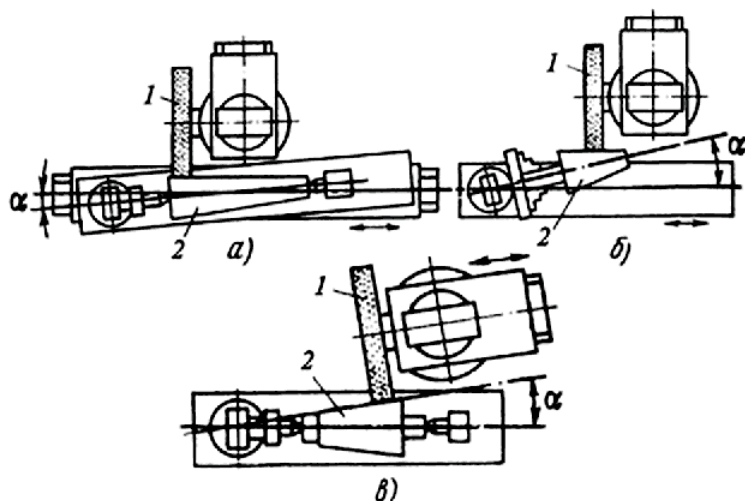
Способы шлифования конических поверхностей на круглошлифовальном станке
